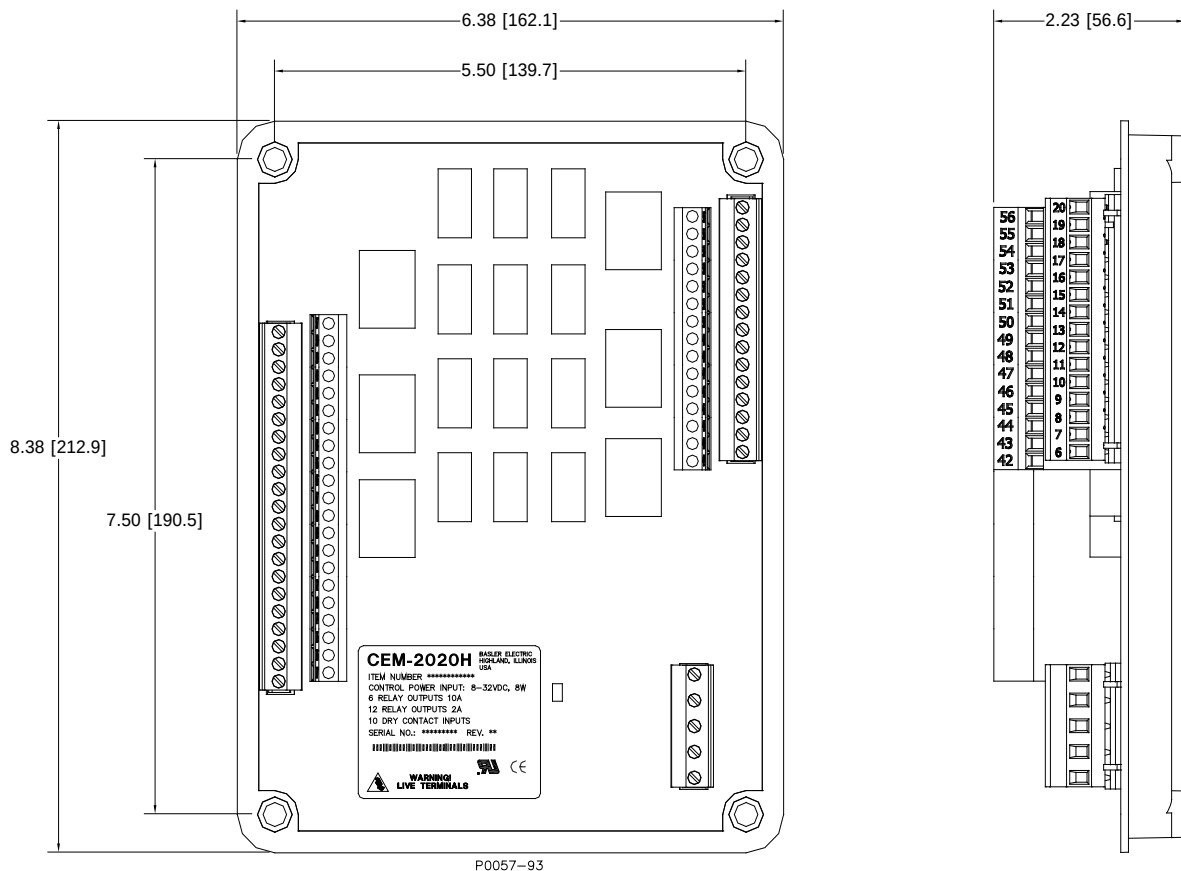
Dimensiones del Conjunto CEM-2020H
